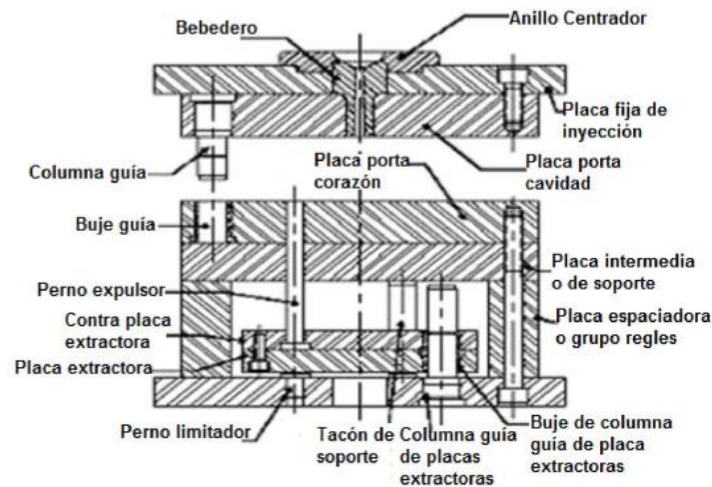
Elementos estructurales de un molde de inyección: Posicionamiento del conjunto de placas [9]
